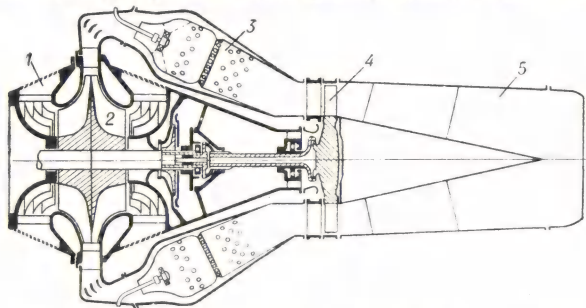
Схема турбореактивного двигателя: 1 — входная часть; 2 — компрессор; 3 — камера сгорания; 4 — турбина; 5 — реактивное сопло.
